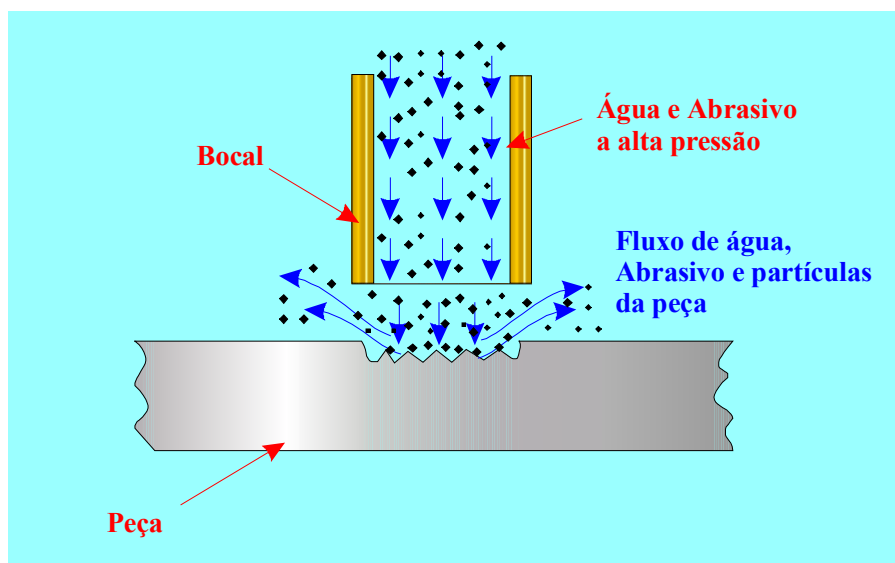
Princípio da Usinagem por Jato d'Água Abrasivo (Tuersley et al, 1994).
